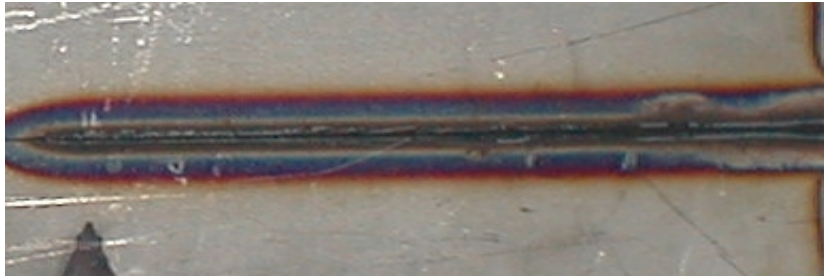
Vista inferior del cordón de soldadura de la muestra enfriada en aire agitado
